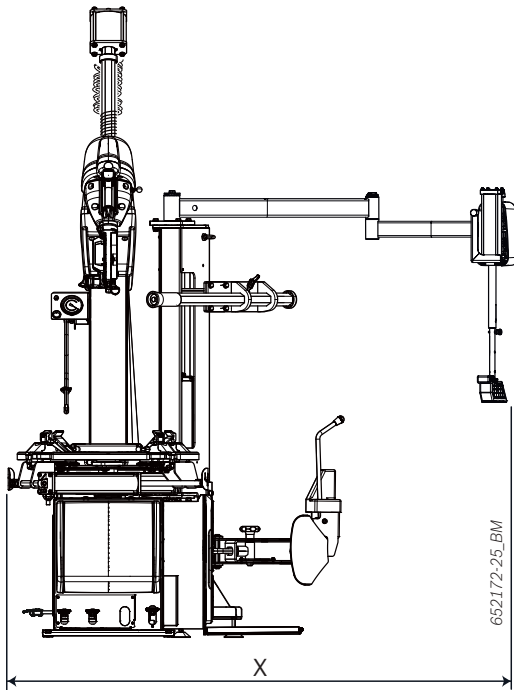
Dimensioni da vista frontale FALCO EVO 628 S (IT) V8
